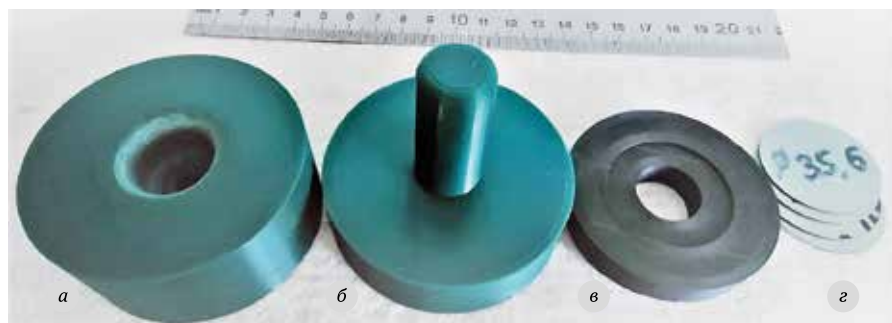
Экспериментальная полимерная оснастка для вытяжки на гидравлическом прессе: а – матрица из PLA; б – пуансон из PLA; в – прижим из нейлона ePA-CF; з – заготовка из стали 12Х18Н10Т
